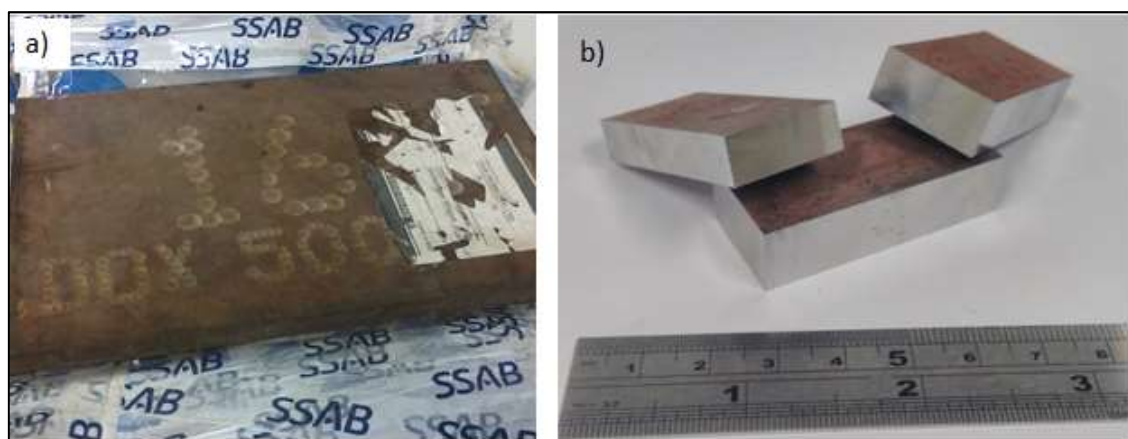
a) Chapa de Hardox®. b) Corpo de Prova após etapa de fresamento.
